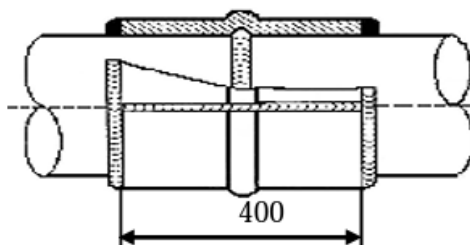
Муфта П3 - Муфта галтельная для ремонта сварных кольцевых швов
